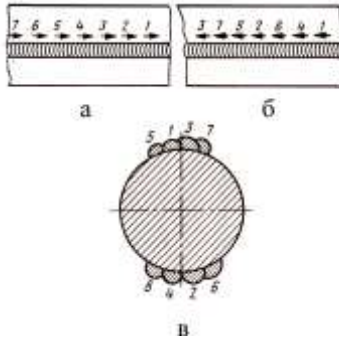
Приклади технологічних прийомів під час зварювання для зменшення деформацій деталей: а – зварювання тонколистового металу ступінчасто в протилежному напрямку; б – зварювання тонколистового металу ступінчасто в напрямку зварки; в – послідовність наплавлення на вал
